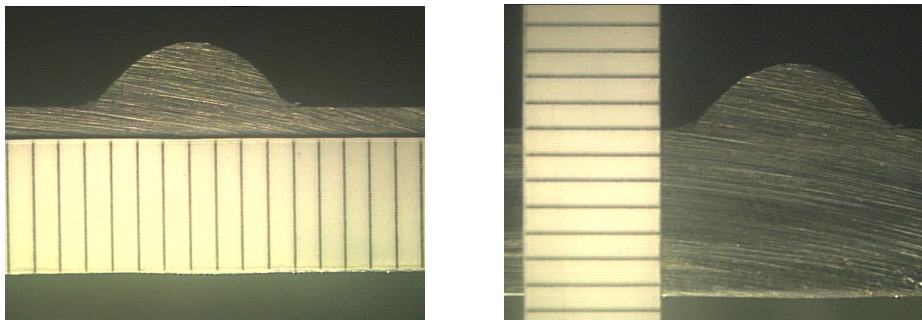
Macrografia de um dos cordões de solda (escala em milímetros).
